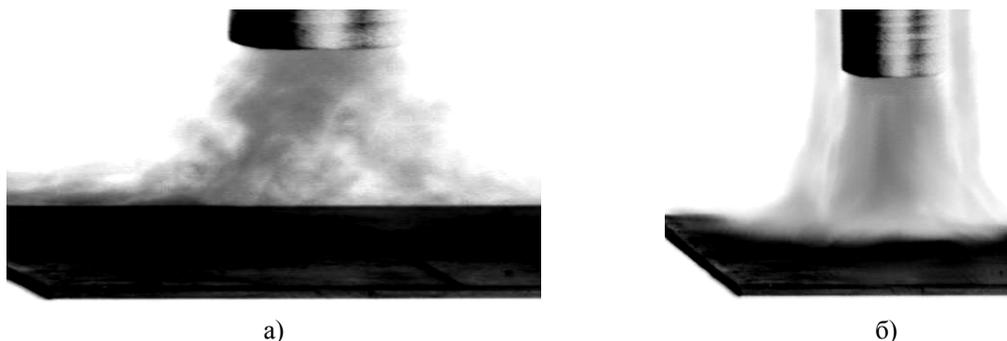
Сварка в защитном газе: а) одноструйная газовая защита; б) двухструйная газовая защита
